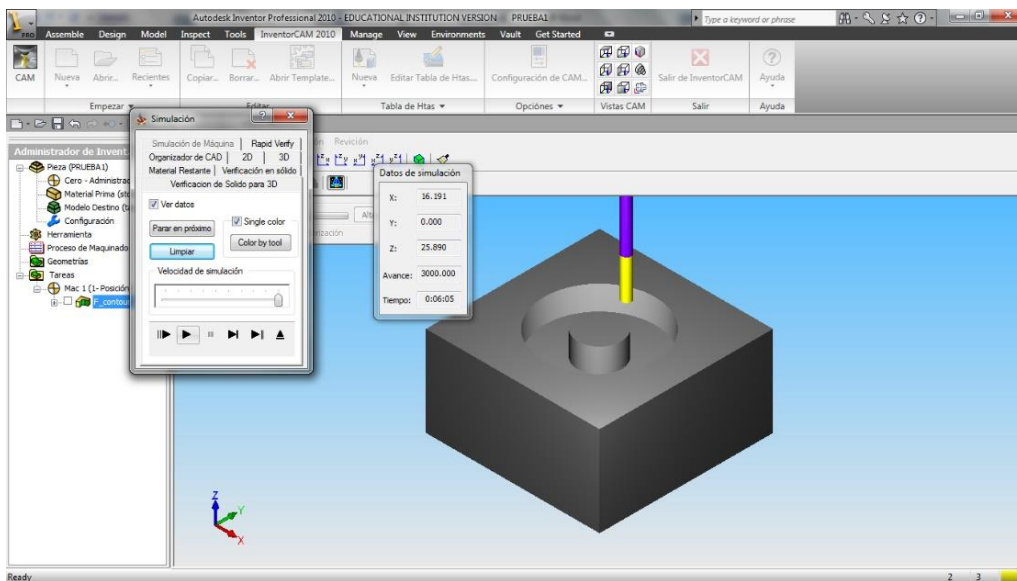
Maquinado Fresadora CNC – Comprobación de desplazamiento de limpieza
